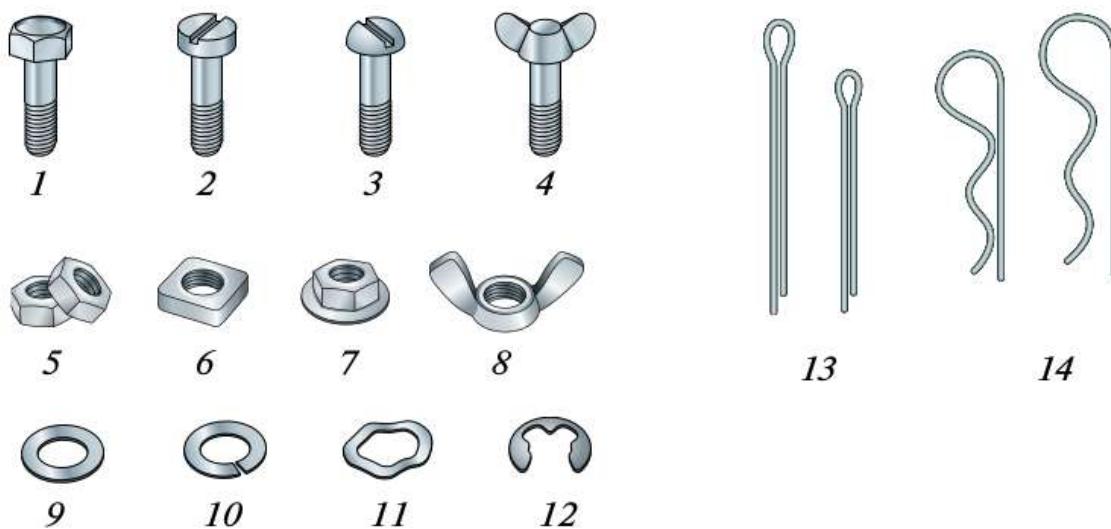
Крепёжные детали: 1 — болт с шестигранной головкой; 2 — винт с цилиндрической головкой; 3 — винт с полукруглой головкой; 4 — винт с барашковой головкой; 5 — гайка шестигранная; 6 — гайка квадратная; 7 — гайка шестигранная с фланцем; 8 — гайка барашковая; 9 — шайба плоская; 10 — шайба пружинная Гровера; 11 — шайба волновая; 12 — шайба быстросъёмная; 13 — шплинты прямые; 14 — шплинты пружинные
